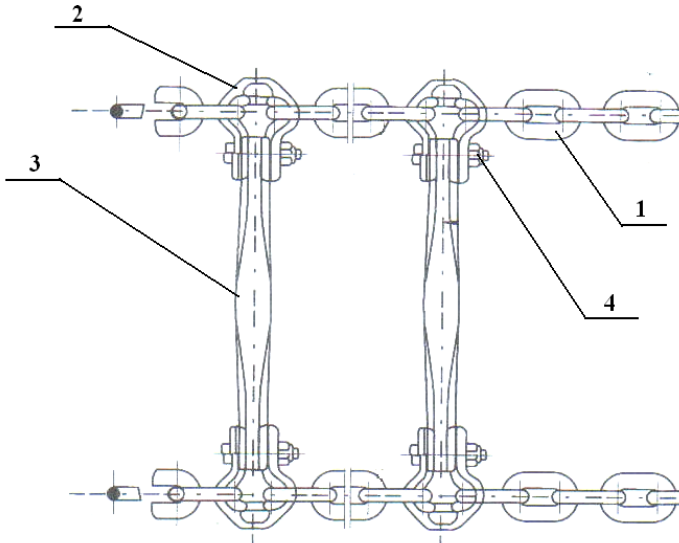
Отрезок скребковой цепи в сборе: 1 - звено цепи; 2 - звено соединительное; 3 - скребок; 4 - соединительный крепёж
